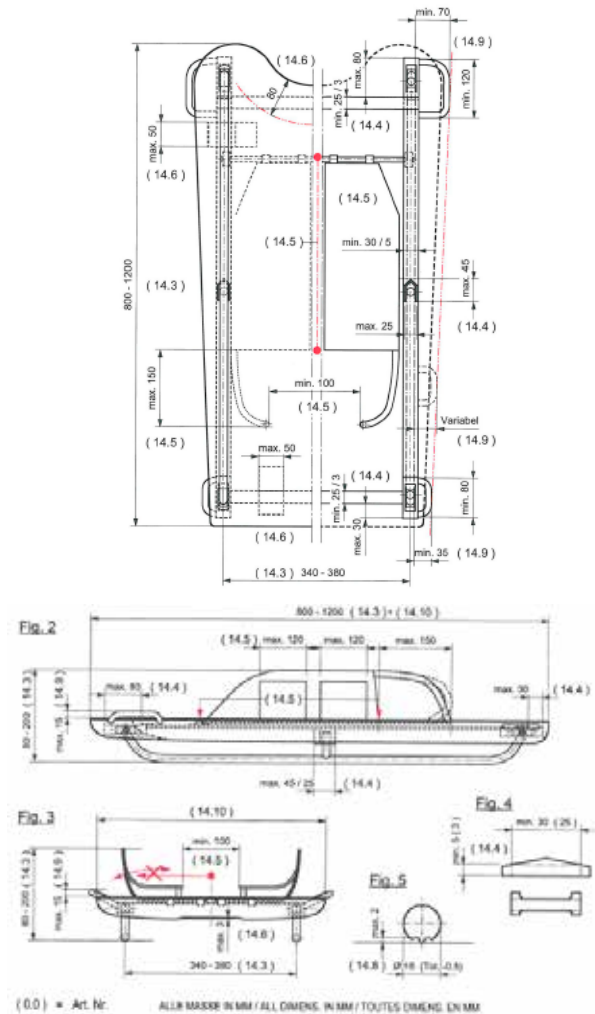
Skizze aus dem Regelwerk zu den autorisierten Bemaßungen des Schlittens; Quelle: [www.fibt.com](http://www.fibt.com)
